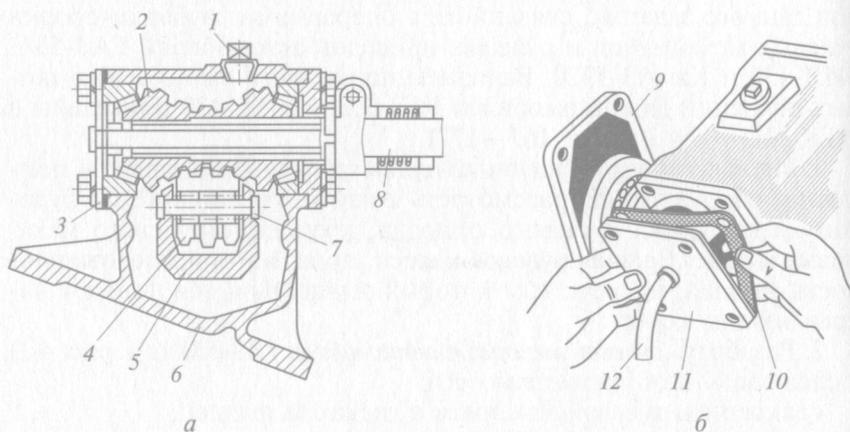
Рулевой механизм автомобиля ГАЗ-53А:
